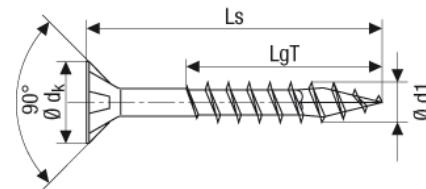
Abmessung Holzschraube (Spax-Produktblatt)
